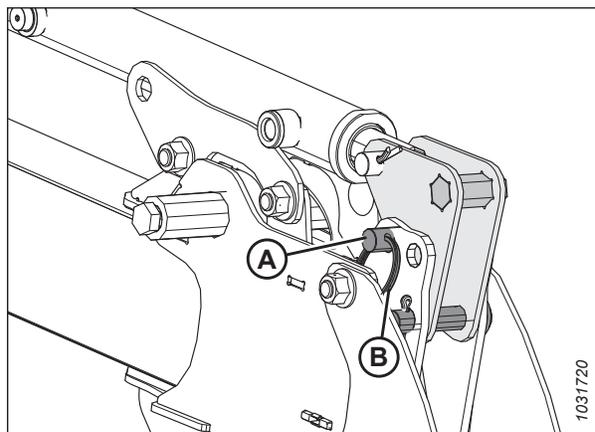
Réglage des vérins avant-arrière de type 1 – Position arrière
